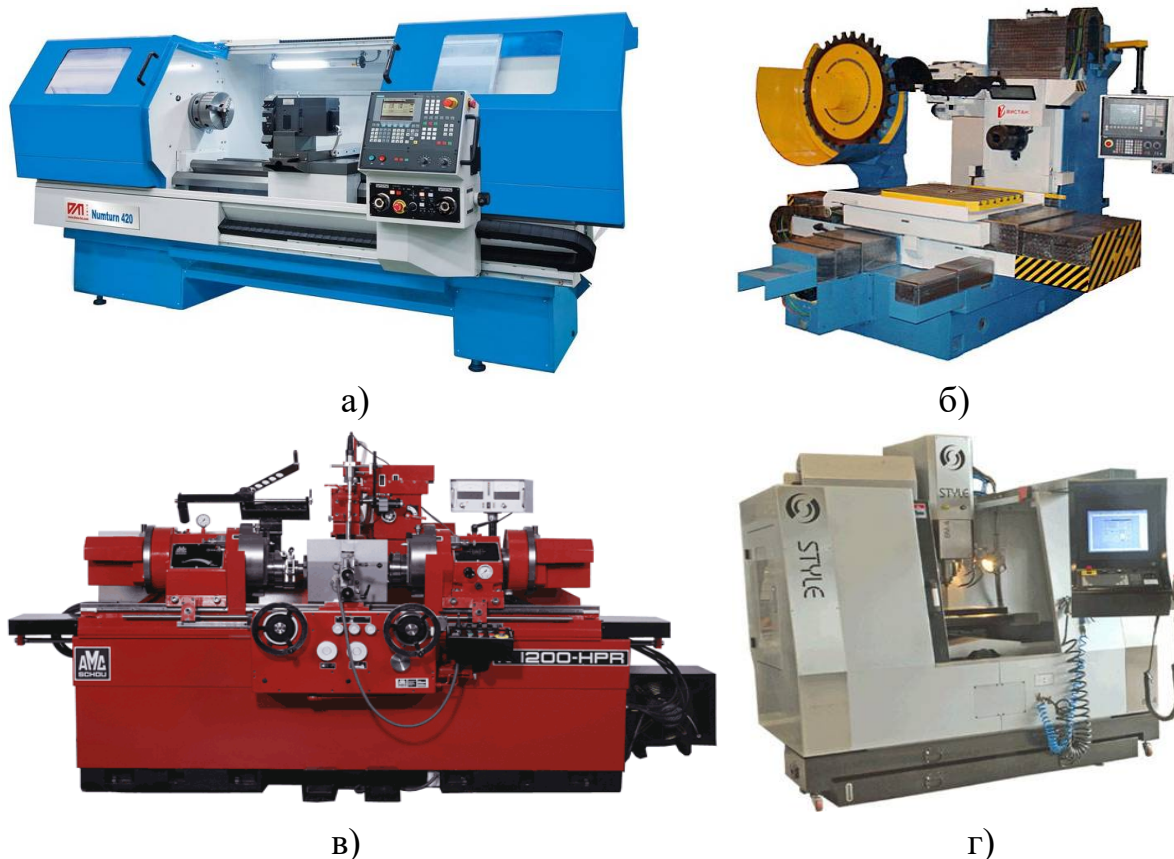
Сучасні верстати основних груп: а – токарний з ЧПК; б – свердлильно-фрезерно-розточувальний з ЧПК; в – круглошліфувальний; г – фрезерний з ЧПК
